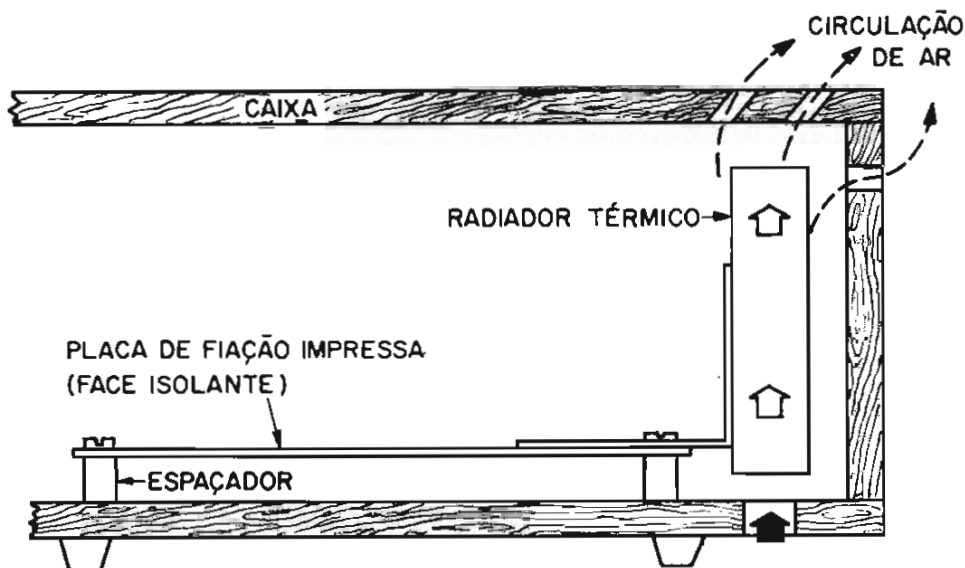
Instalação do módulo amplificador em uma caixa de madeira.
